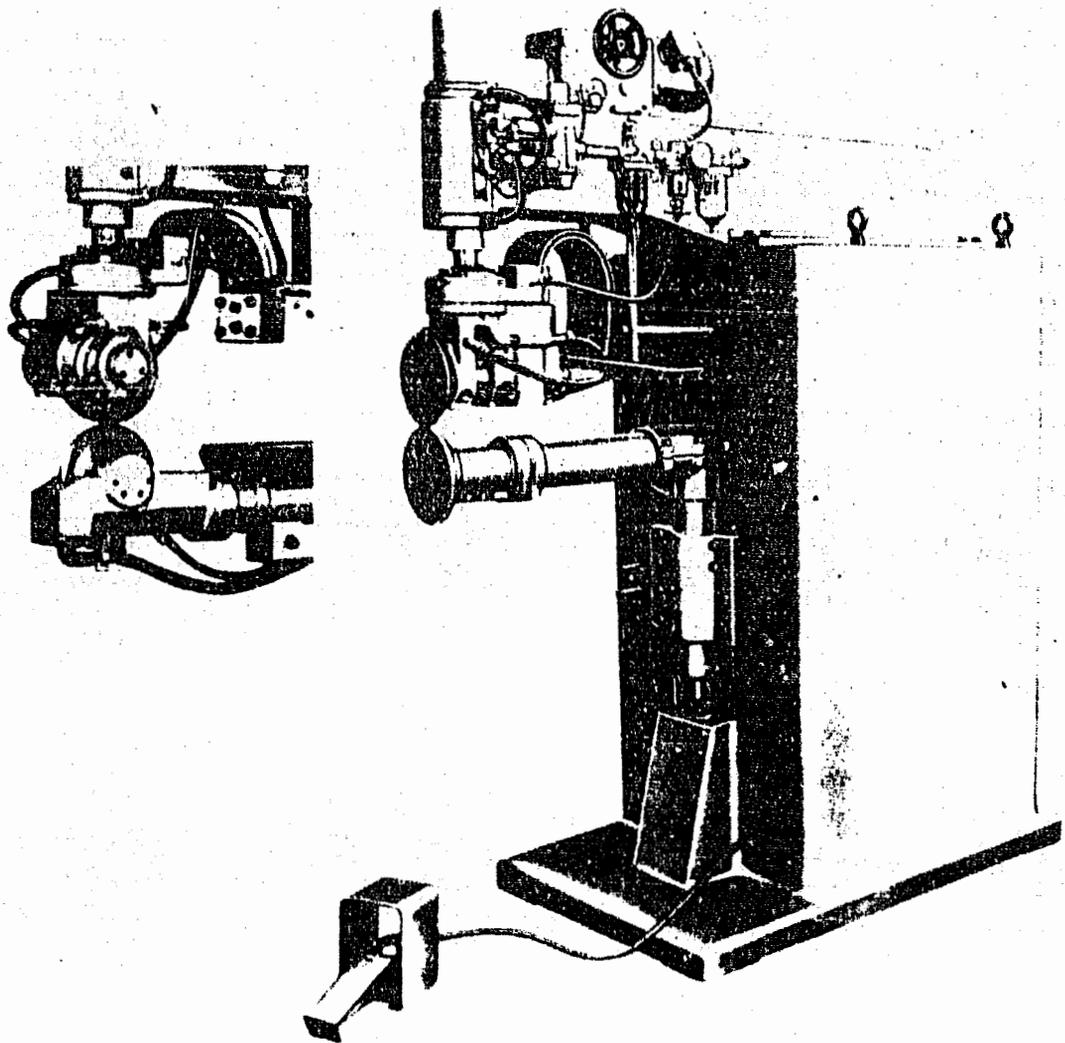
Máquina estacionaria para soldadura por costura, adaptable para soldar transversal y longitudinalmente.
